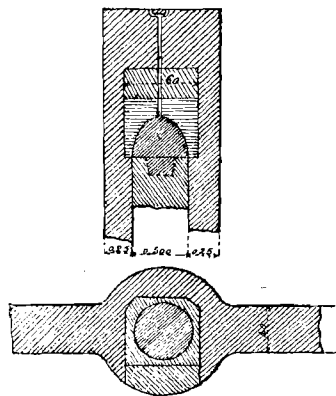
et 5. — Coupes longitudinale et transversale du pivot avec rehaussement.
